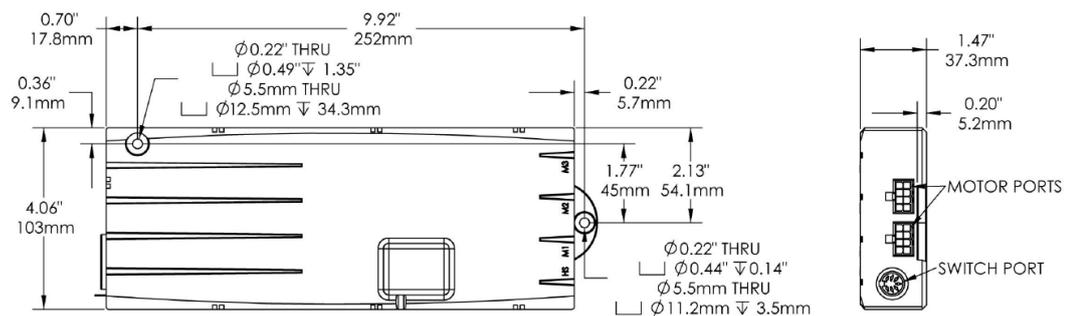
Abmessungen und Anschlüsse der Motorsteuerung
